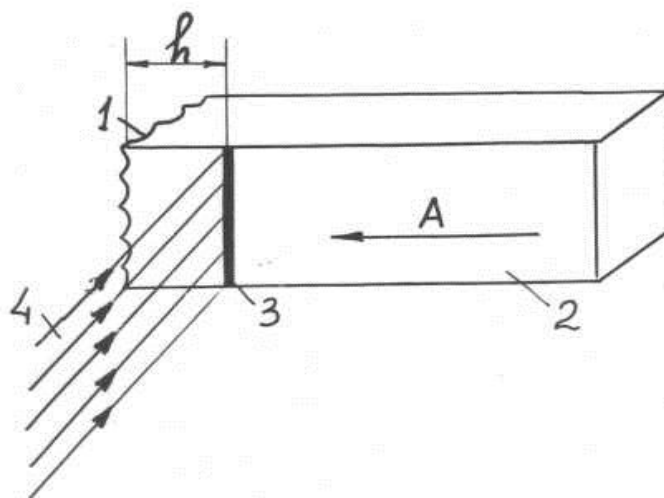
Схема съемки шлифа, расположенного нормально к поверхности излома:
